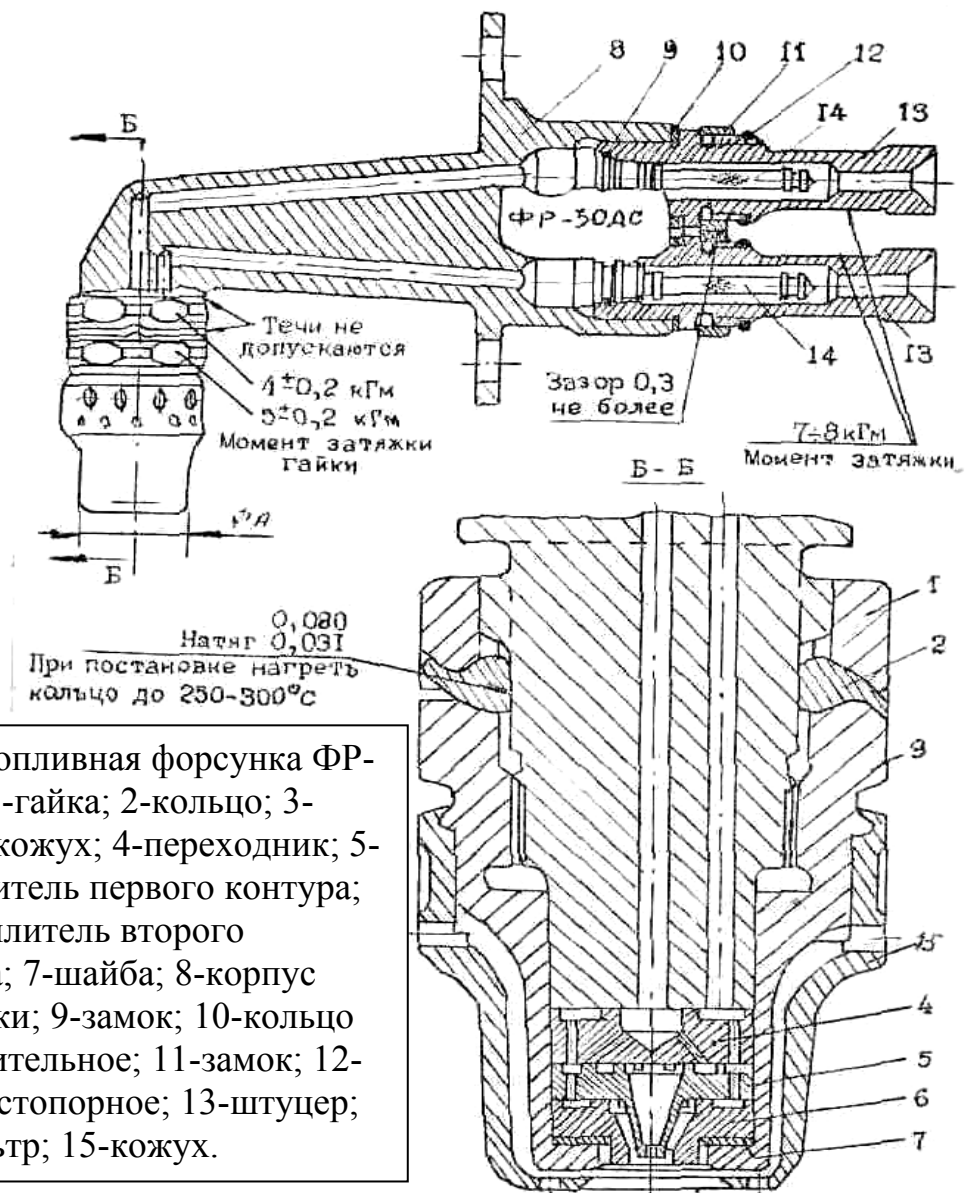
Топливная форсунка ФР-30ДС: 1-гайка; 2-кольцо; 3-стакан-кожух; 4-переходник; 5-распылитель первого контура; 6-распылитель второго контура; 7-шайба; 8-корпус форсунки; 9-замок; 10-кольцо уплотнительное; 11-замок; 12-кольцо стопорное; 13-штуцер; 14-фильтр; 15-кожух.
